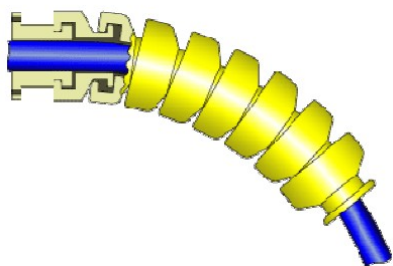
Обхватываемая конструкция соединения ограничителя изгиба
